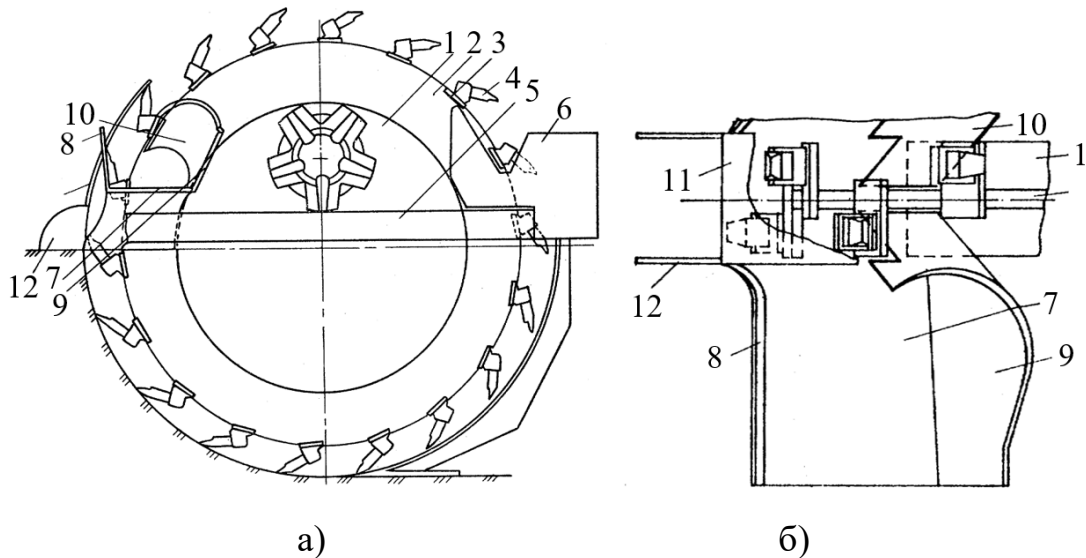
Робочий орган роторного екскаватора з двоступеневим розвантаженням: а) – вид з боку; б) – вид зверху; 1 – ротор; 2 – диск центральний; 3 – траверса; 4 – ґрунторозробний різець; 5 – рама; 6 – бермоутворювач; 7 – основа лотка; 8 – стінка передня лотка; 9 – стінка задня лотка; 10 – ґрунтознімач; 11 – перемичка передня; 12 – щитки захисні
